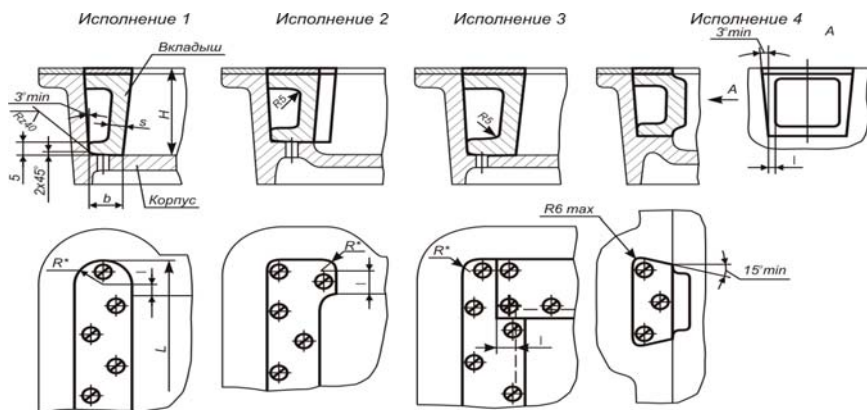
Примеры крепления вкладышей в корпусе стержневого ящика
